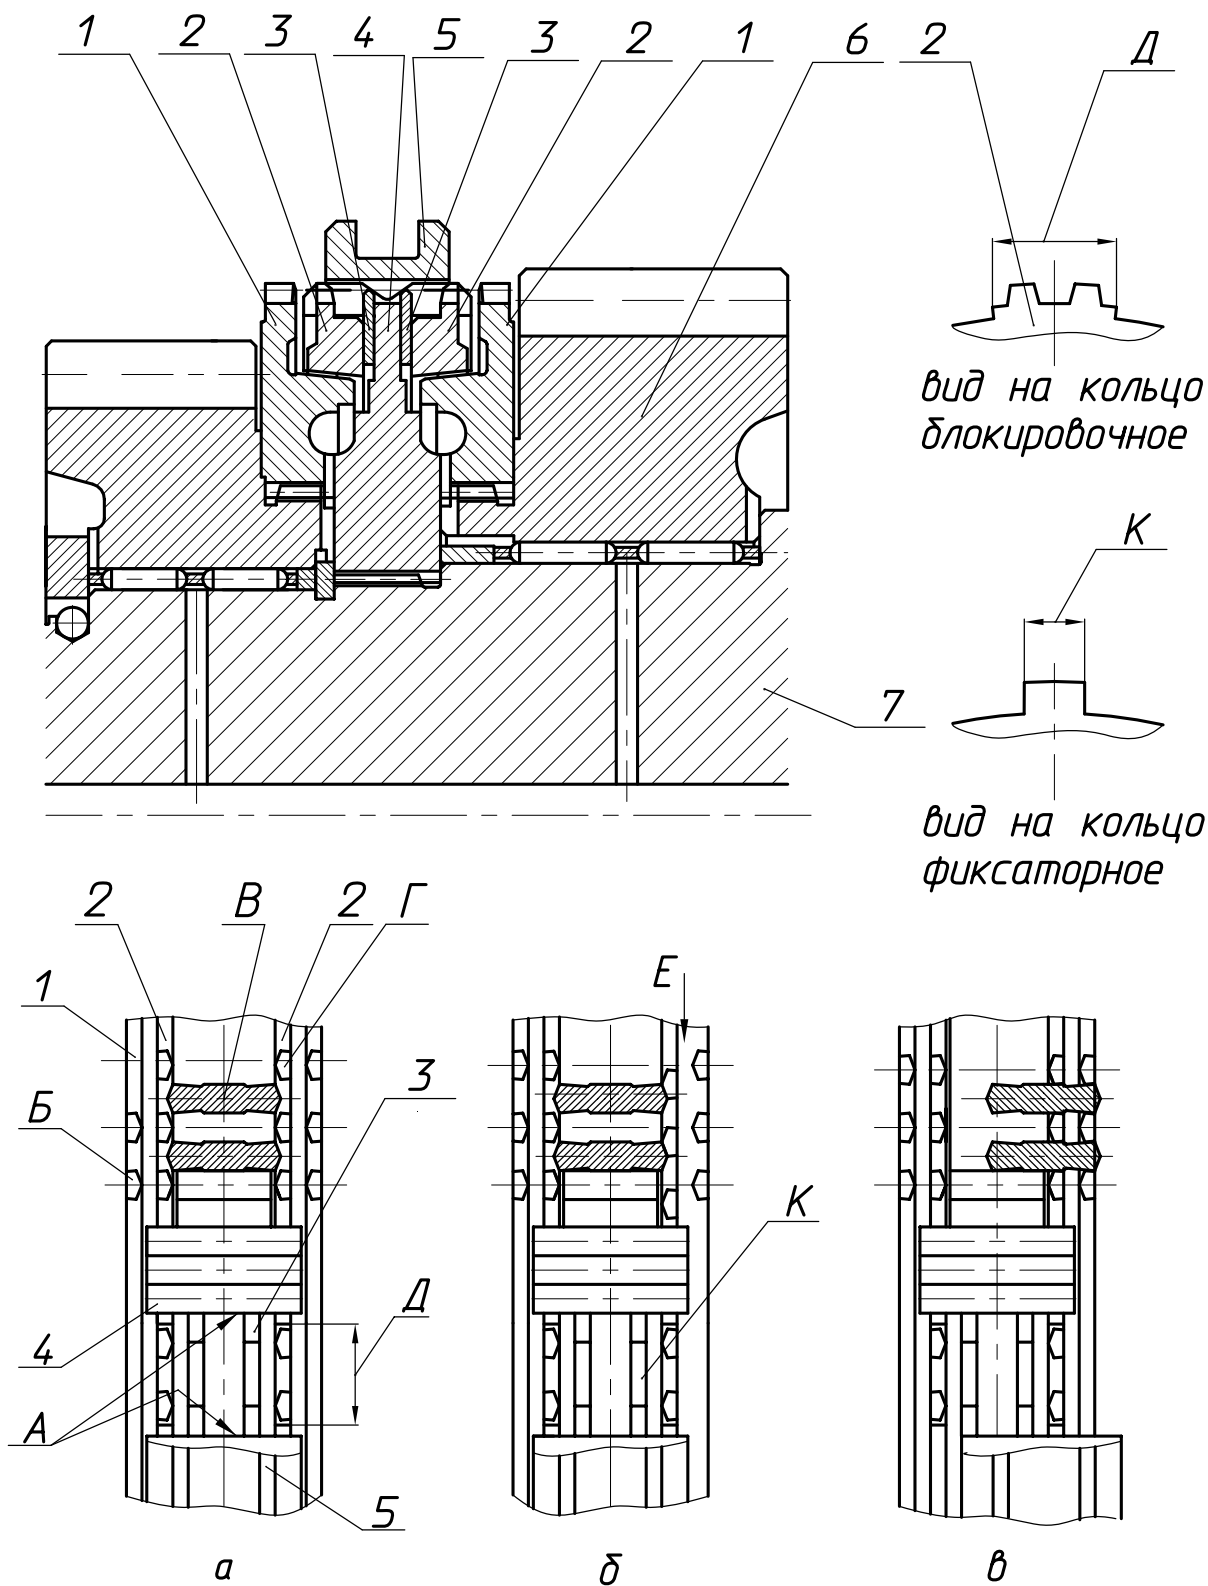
Устройство и схема действия синхронизаторов КП типа ЯМЗ-239
